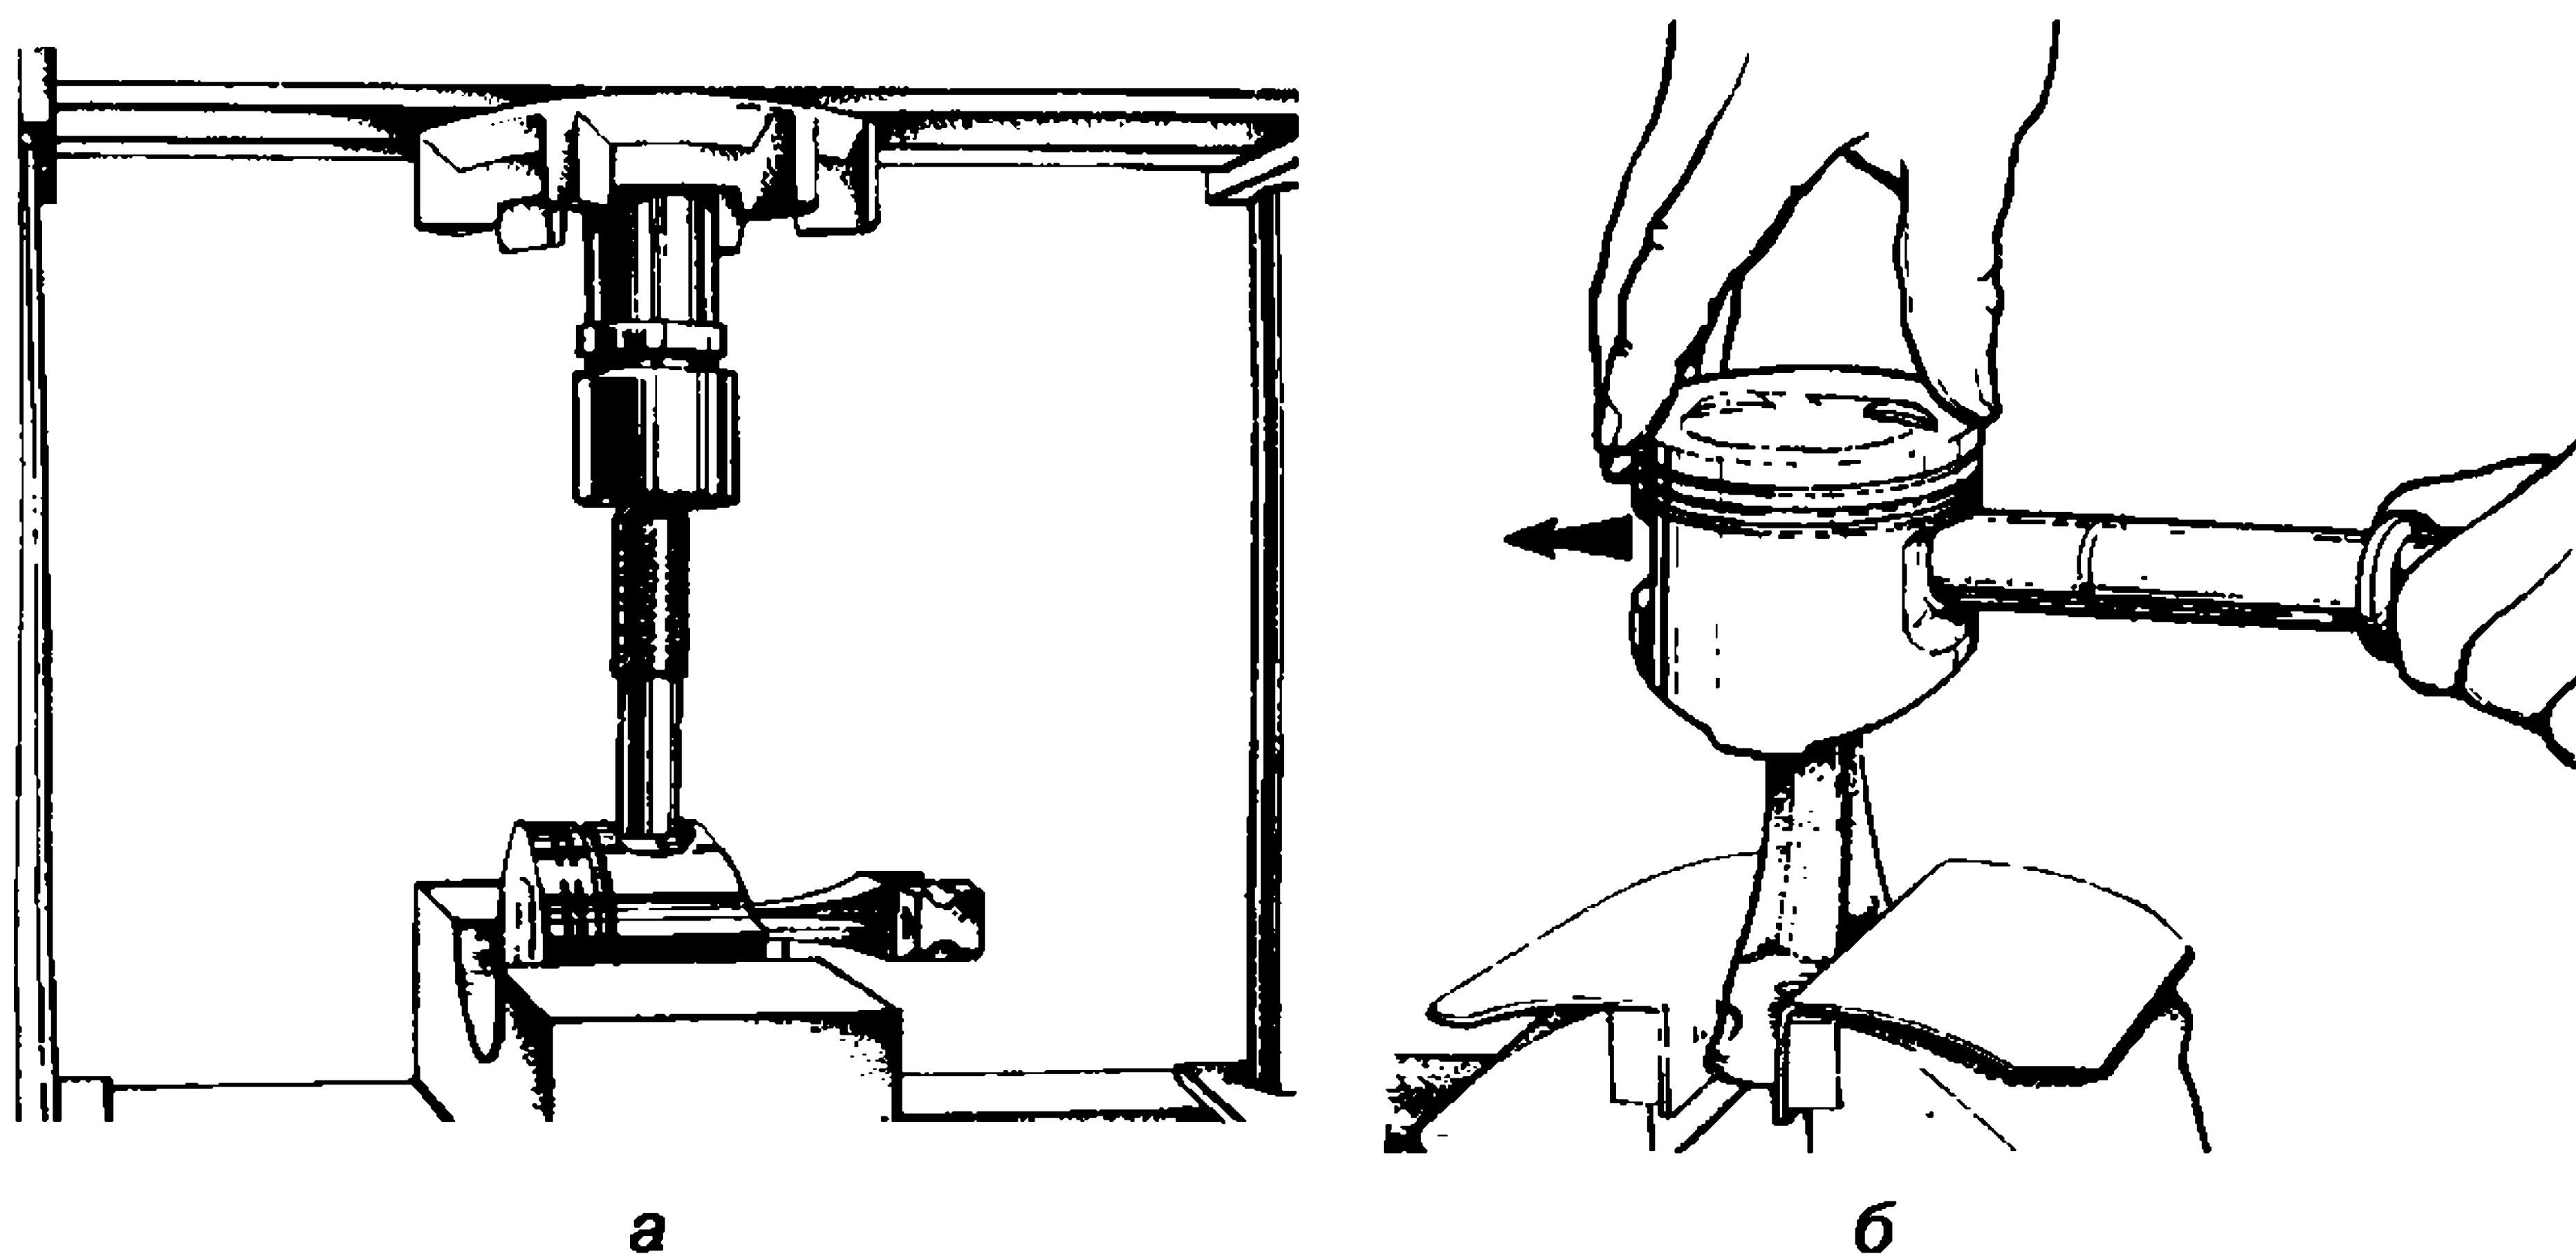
Выпрессовка (а) и запрессовка (б) поршневого пальца
